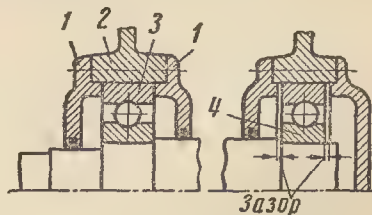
Подшипниковые узлы на шарикоподшипниках.
